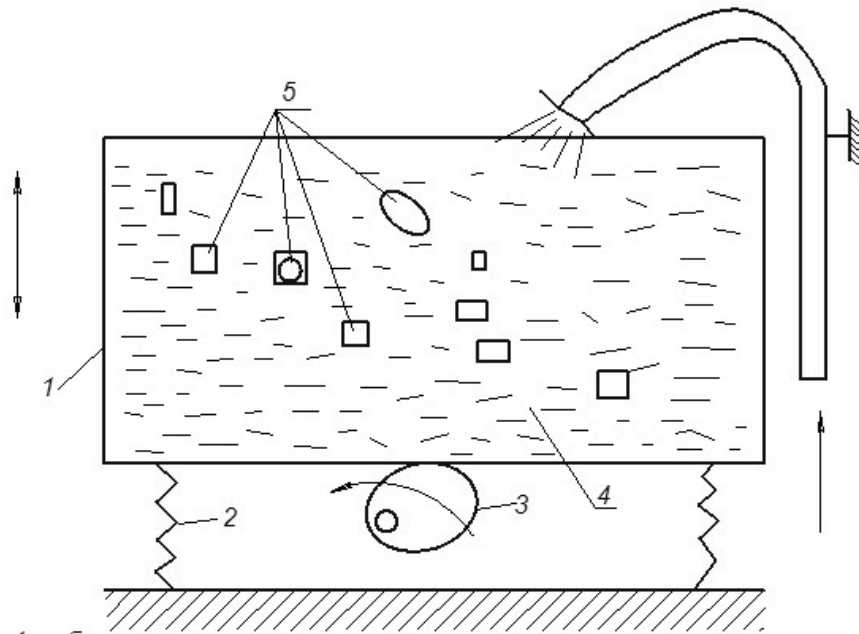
Схема віброабразивного оброблення: 1 – робоча камера; 2 – пружина; 3 – незбалансований вал; 4 – робоче середовище; 5 – оброблювані деталі.
